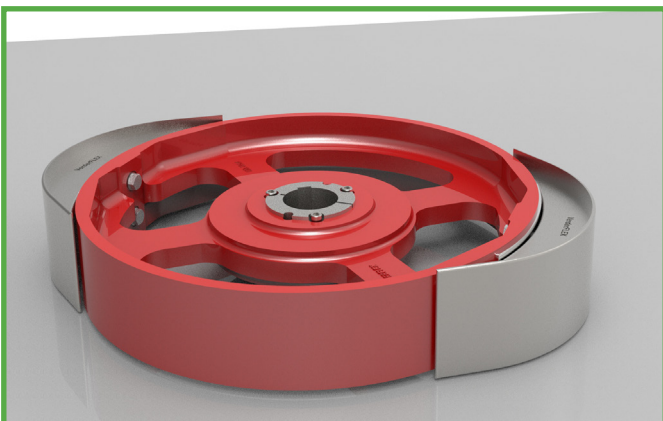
Montage des sabots du rotor sur le rotor (étape 3)
